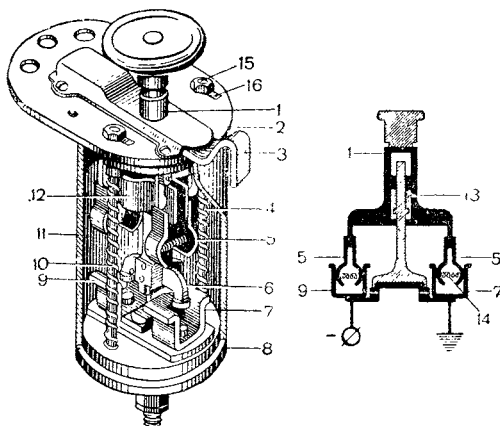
Выключатель батарен ВВ-404 (разрез и схема):
